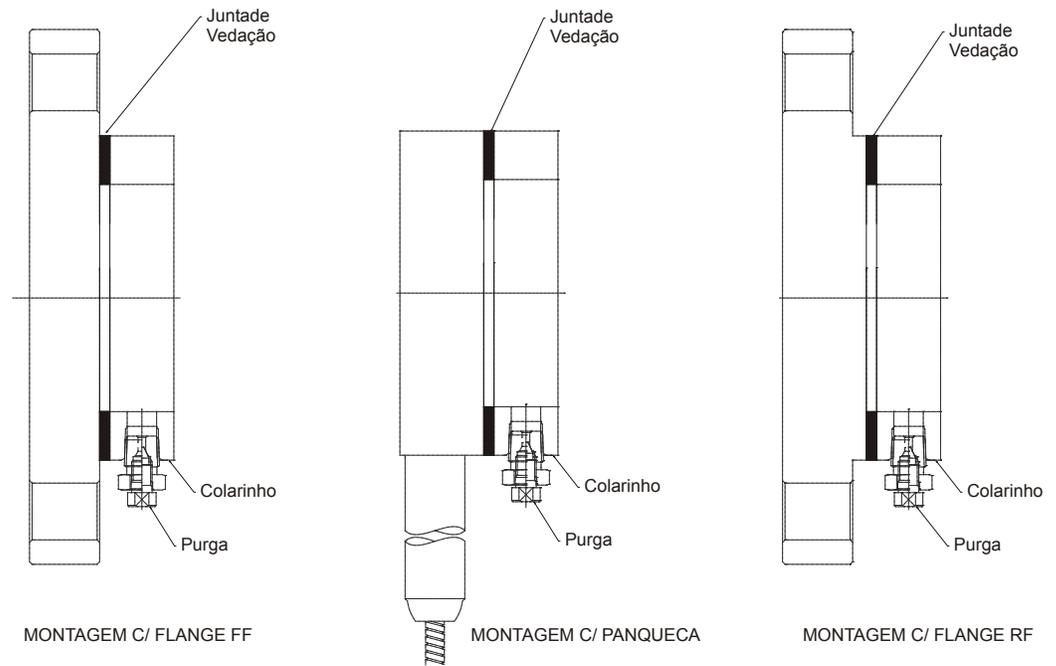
Vista em corte das Montagens com Juntas e Conjunto do Purgador
